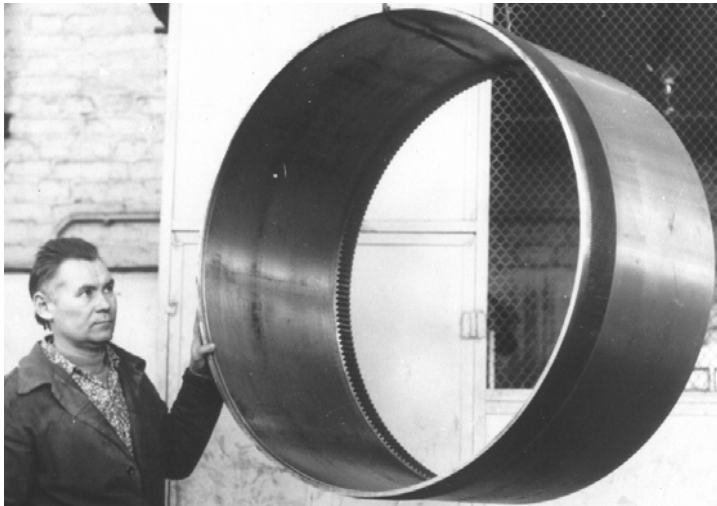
Гибкое колесо волнового редуктора поворота миксера МП-600АС
